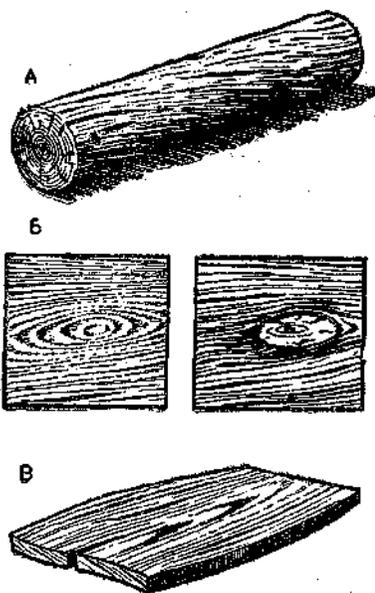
Пороки древесины: А — косослой; Б — сучок здоровый (слева) и выпадающий (справа); В — трещины и коробление в результате неравномерной усушки.
